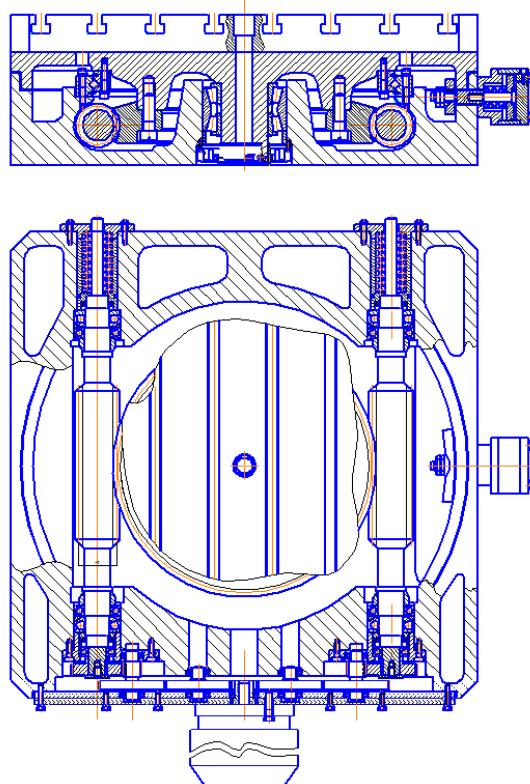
Поворотный стол для станка 65А90ПМФ4
